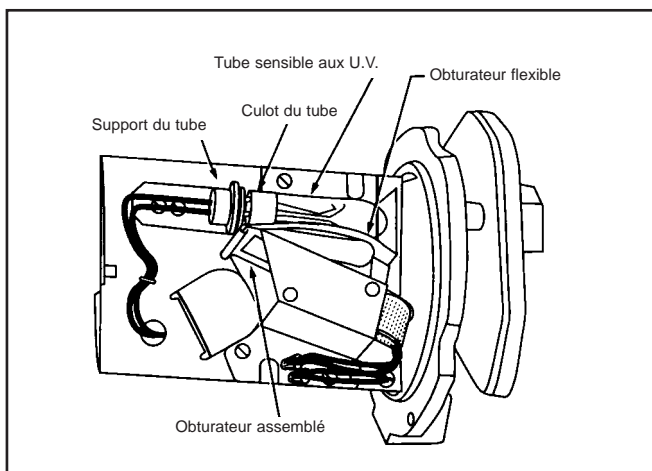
Remplacement du tube sensible aux rayons ultraviolets.
